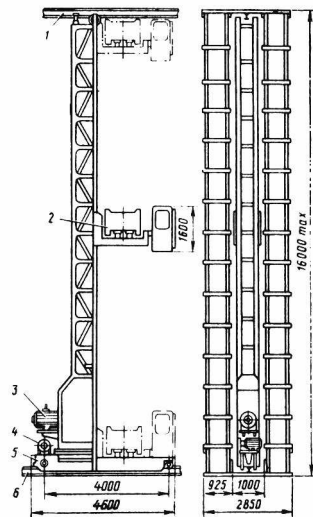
Стеллажный кран-штабелер с одной грузоподъемной колонной с опорой на напольный рельс
